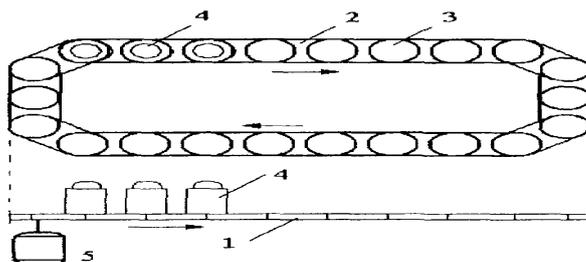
Схема пластинчатого транспортера: 1 - приводная цепь с пластинами; 2 - пластина типа; 3 - пластина типа; 4 - перемещаемый предмет; 5 – привод
